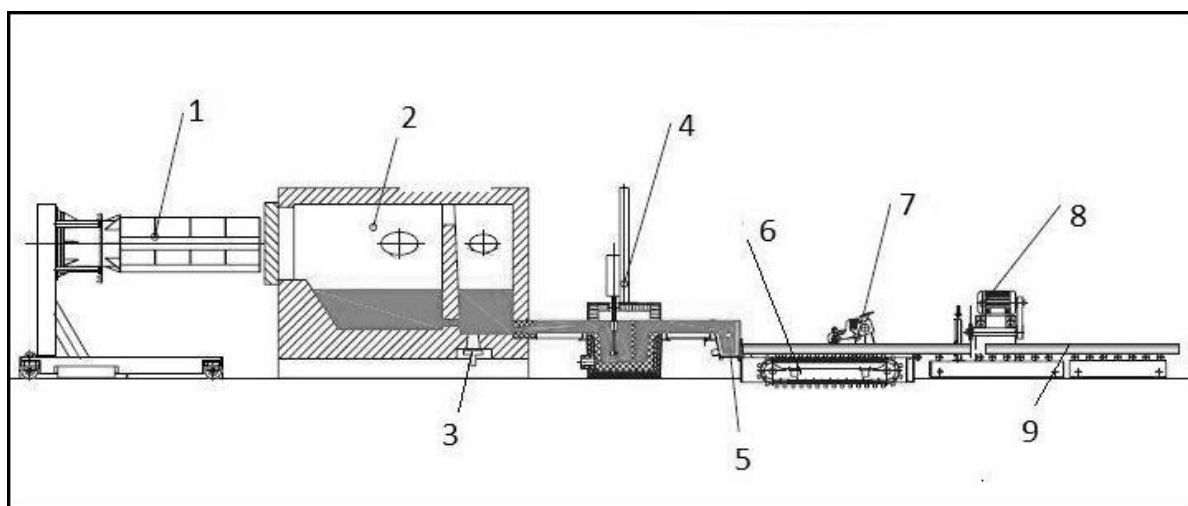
Схема установки для горизонтального лиття злитків компанії Hertwich Engineering: 1 – завантажувальна машина; 2 – двокамерна піч; 3 – пориста діафрагма у подіні ливарної камери печі; 4 – установка для позапічної обробки розплаву; 5 – металоприймач з блоком кристалізаторів; 6 – транспортер; 7 – притискні ролики; 8 – летуча дискова пила; 9 – злиток.
